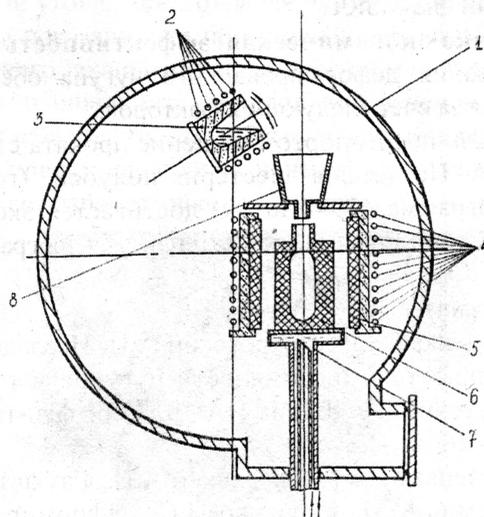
Схема установки для направленной кристаллизации: 1 - вакуумная камера; 2 - плавильный индуктор; 3 - плавильный тигель; 4 - кристаллизационный индуктор; 5 - графитовый нагреватель; 6 - графитовая изложница; 7 - водоохлаждаемый шток; 8 - заливающая чаша
